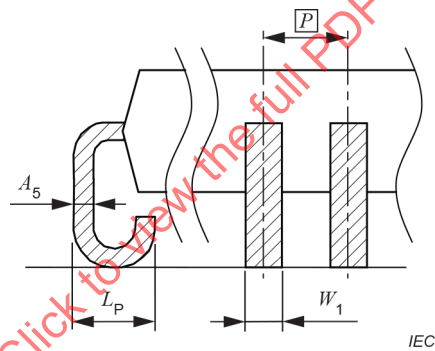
Définitions des dimensions des types de bornes à partie basse plane
